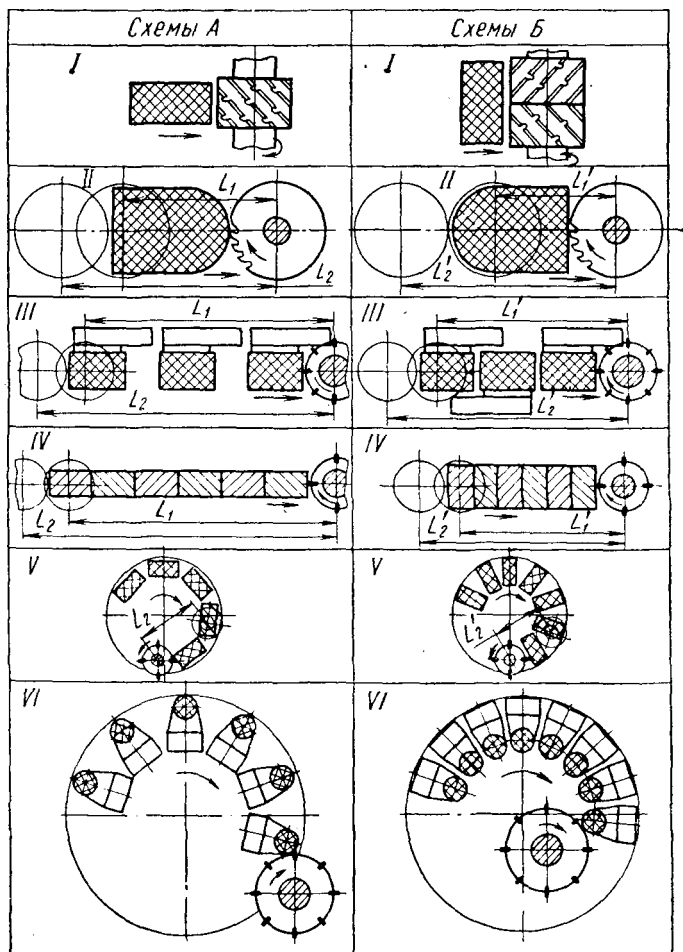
Зависимость рабочего хода инструмента от расположения деталей в приспособлениях при фрезеровании
